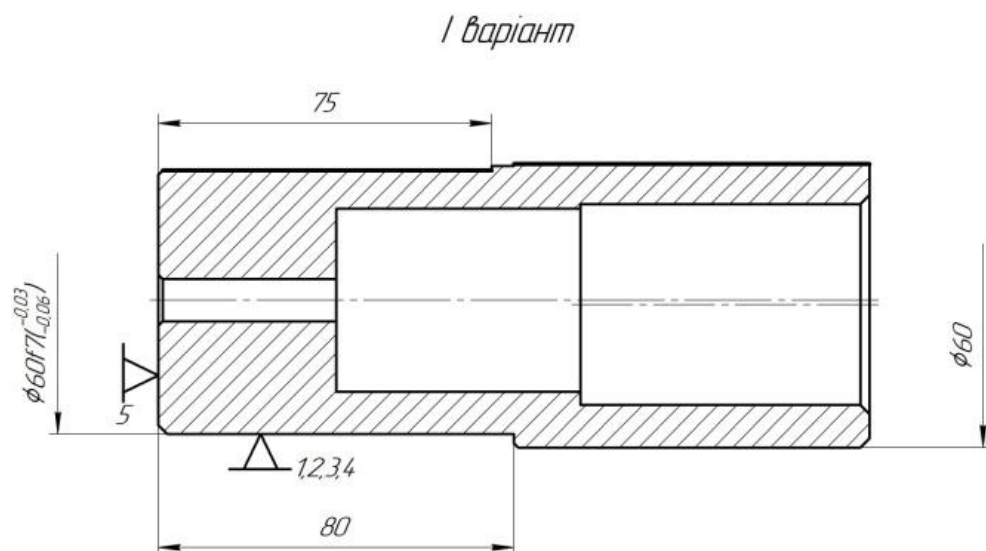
Схема базирования заготовки на фрезерной операции I вариант
